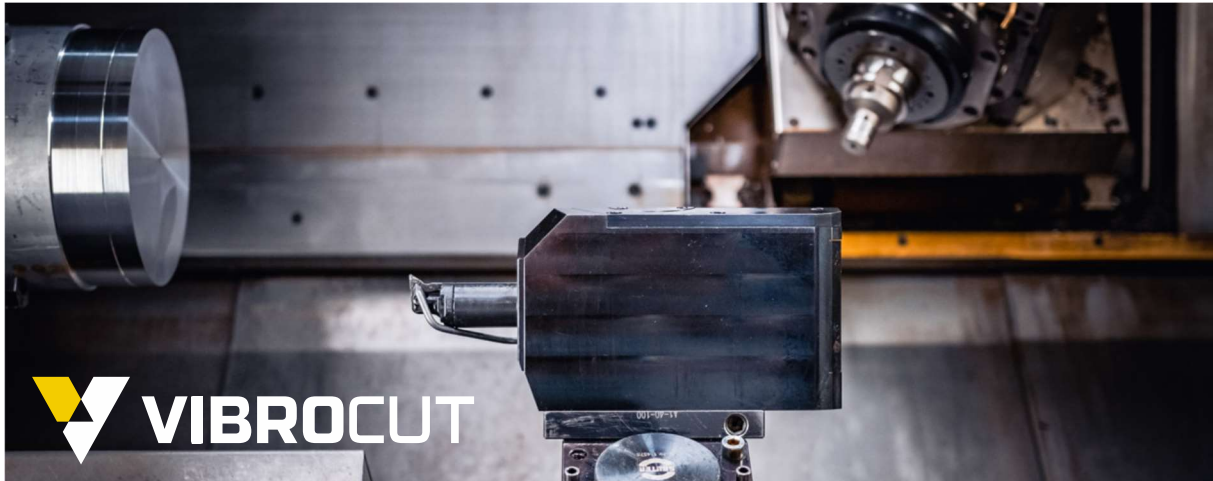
VIBROturn mit Bohrstanze für die Innenbearbeitung
